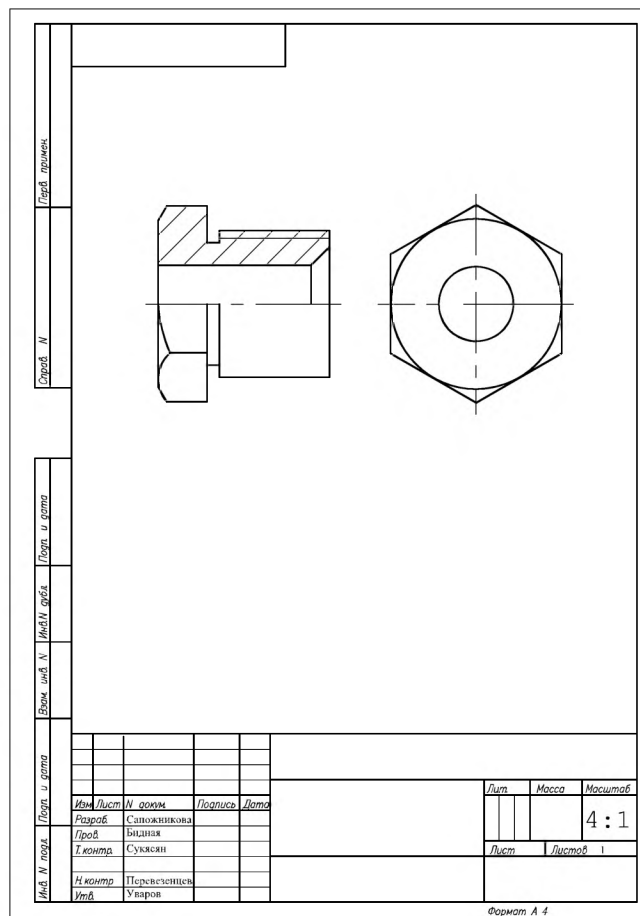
Увеличенный чертеж штуцера, помещенный в форматку А4
